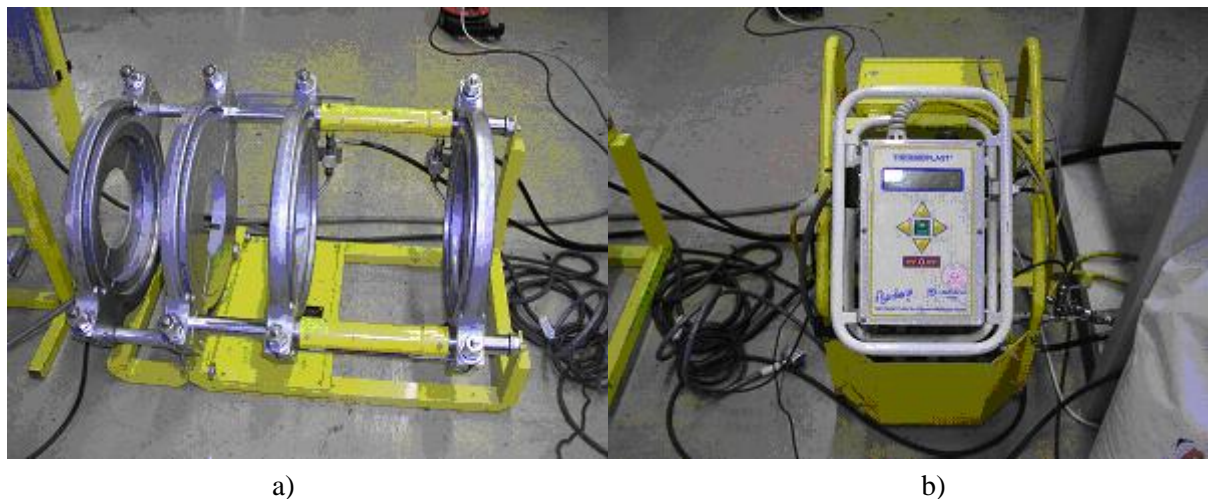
banc de soudage (a) et boîtier de contrôle (b)
